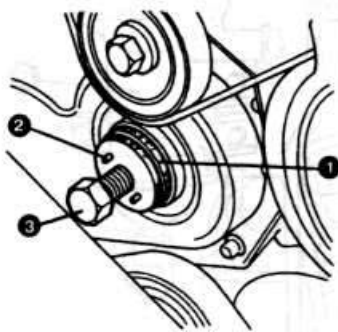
Выпрессовка вала ТНВД из шестерни привода:
